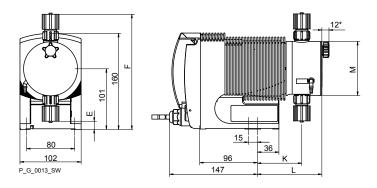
Габаритный чертеж датта/L, исполнения из материала РРЕ, РРВ - размеры в мм
